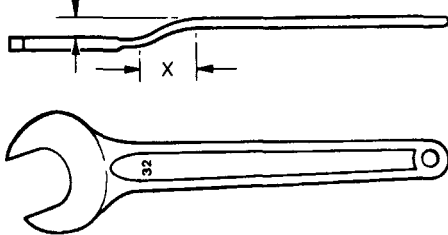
Выгнутый гаечный ключ для снятия вентилятора с рядного двигателя.
